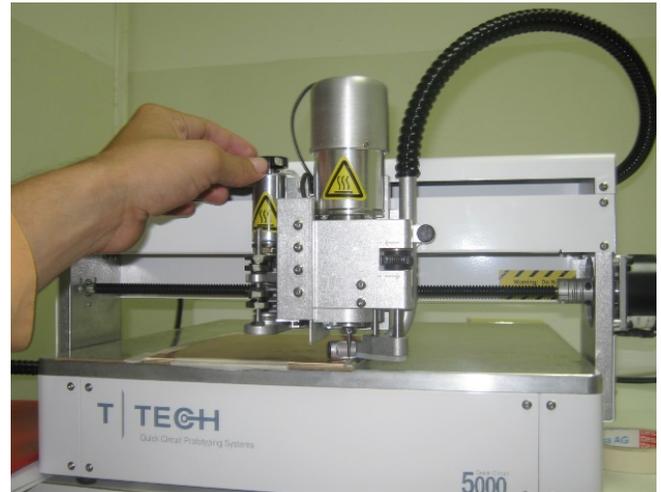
Máquina CNC de tres ejes para fabricación de PCB.
